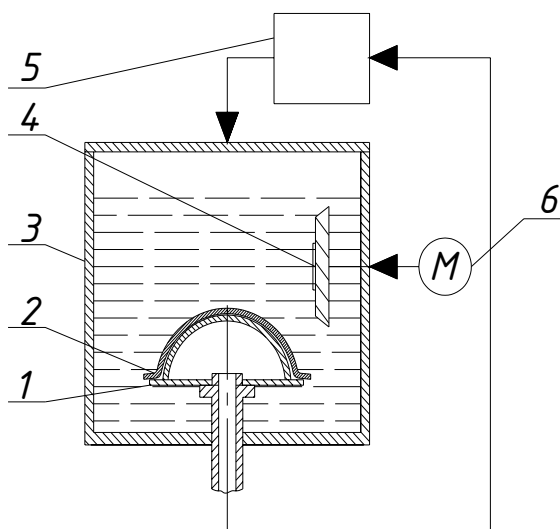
Схема пристрою для гідромеханічного формування: 1 – формуючий елемент; 2 – деталь швейного виробу; 3 – камера для формування; 4 – активатор; 5 – вузол подачі та відсмоктування РАРС; 6 – двигун
